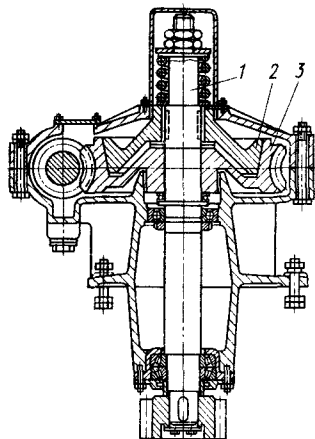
Предохранительная фрикционная коническая муфта червячного редуктора механизма поворота крана
